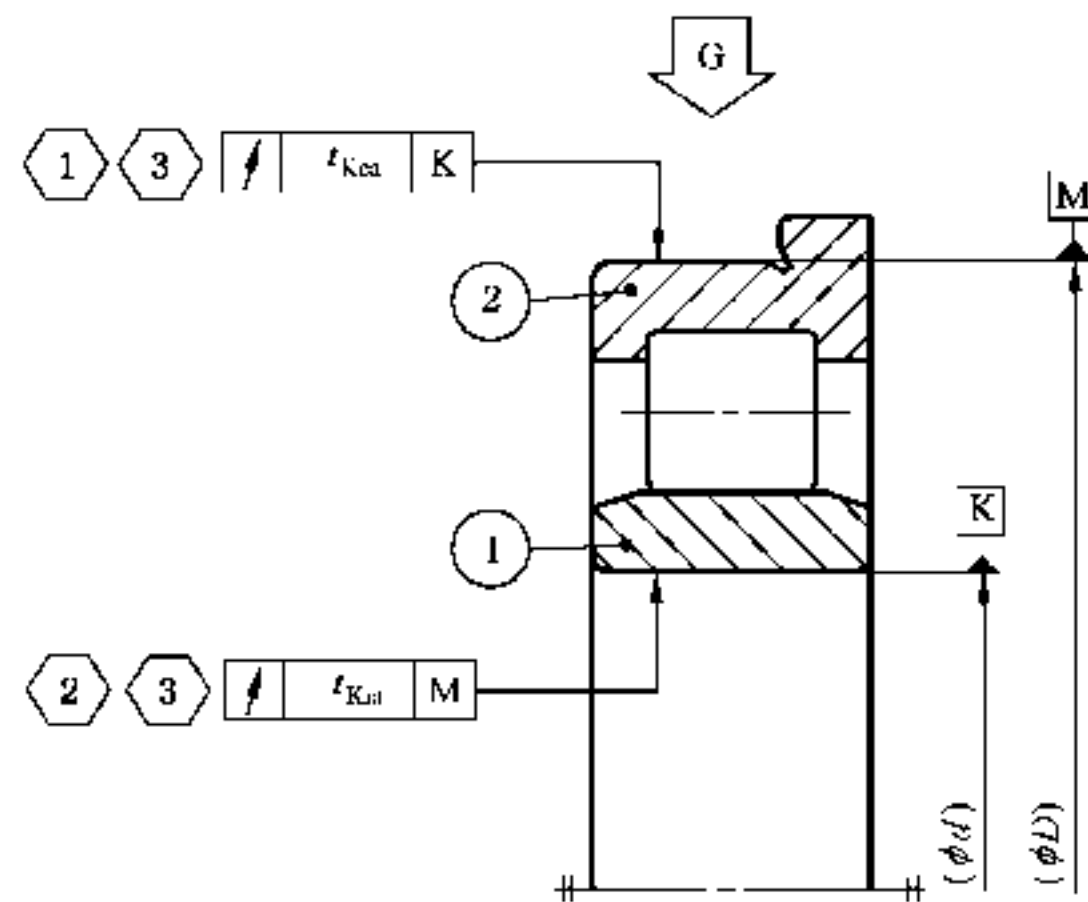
凸缘外圈轴承单个部件的几何公差
